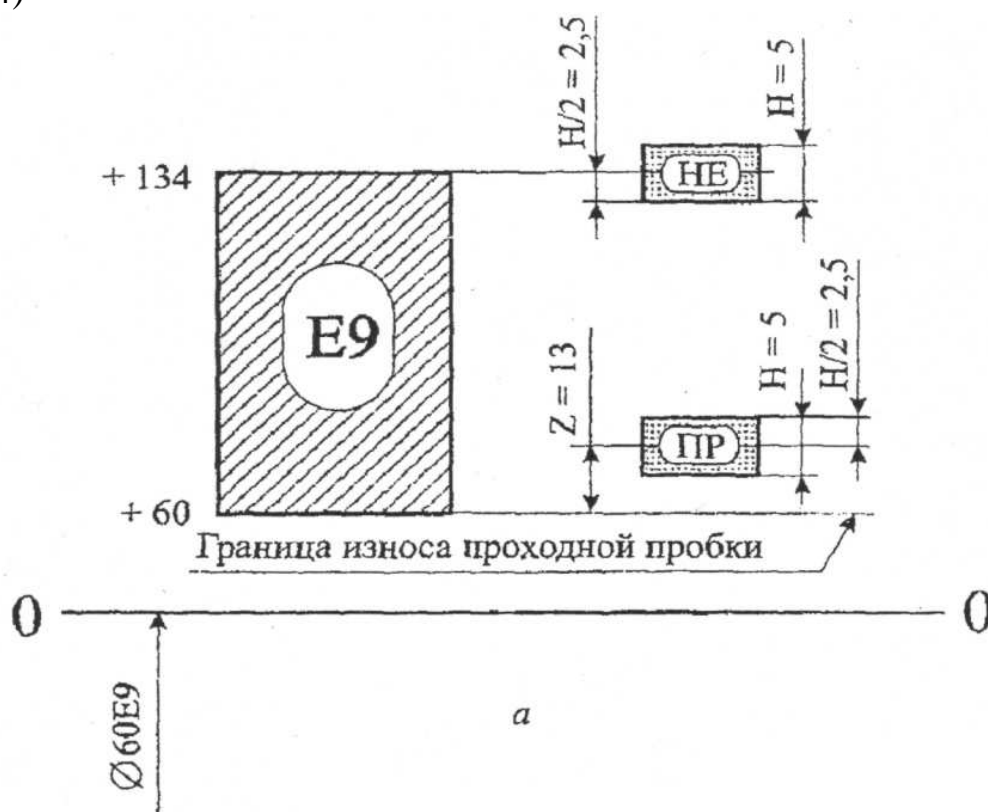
Расположение полей допусков гладких калибров для контроля отверстия $\varnothing 60E9$
